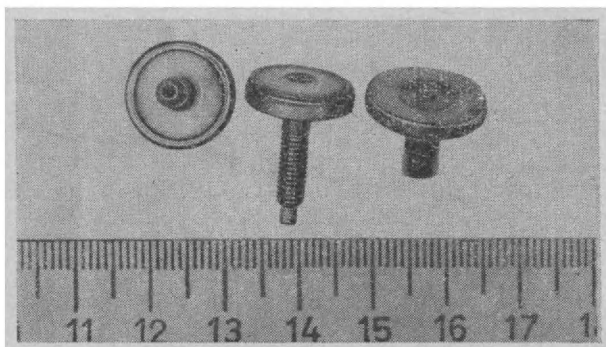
Концентрический комбинированный спай. Металлические детали изготовлены из стали; стеклянные детали получены из свинцового стекла (8) стеклопорошковым методом. Ввод изготовлен из трубочки, которая перед впаиванием подверглась меднению.
